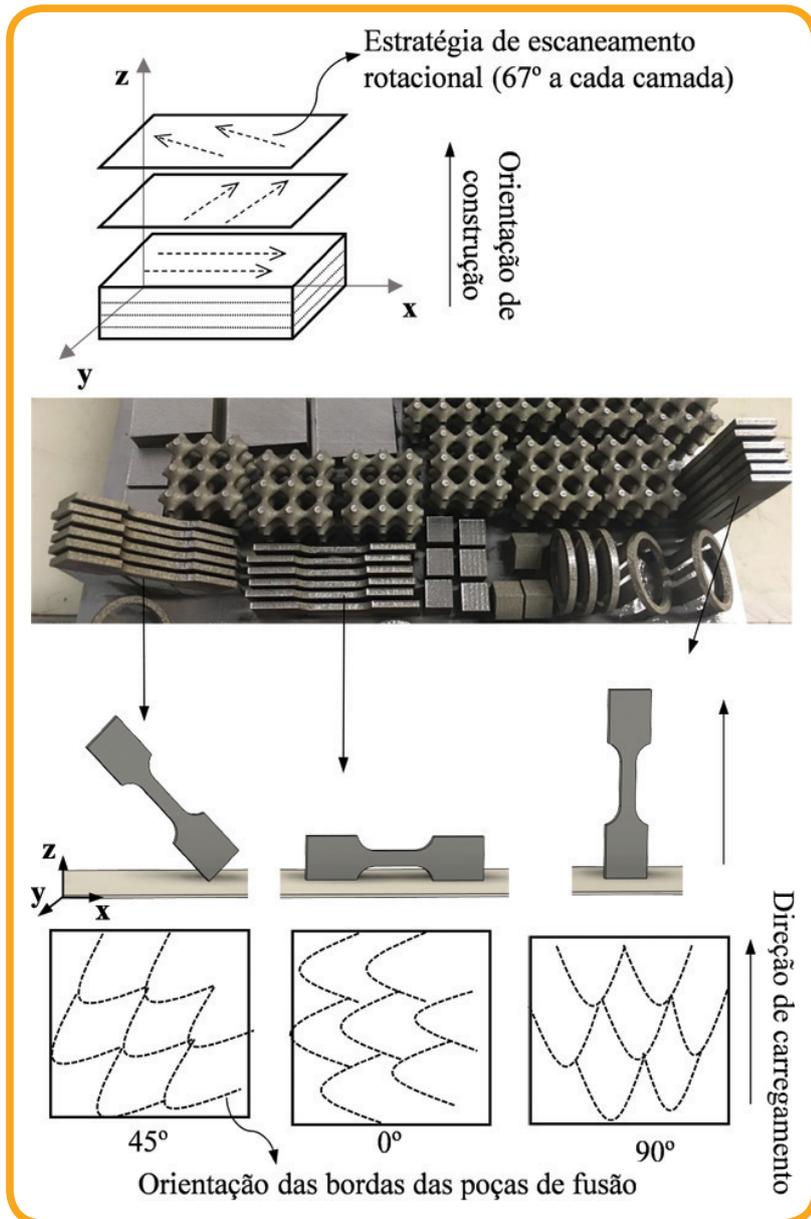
Orientações de construção e estratégia de escaneamento do laser utilizadas na manufatura aditiva. Fonte: Traduzido de Oliveira et al. [1].
